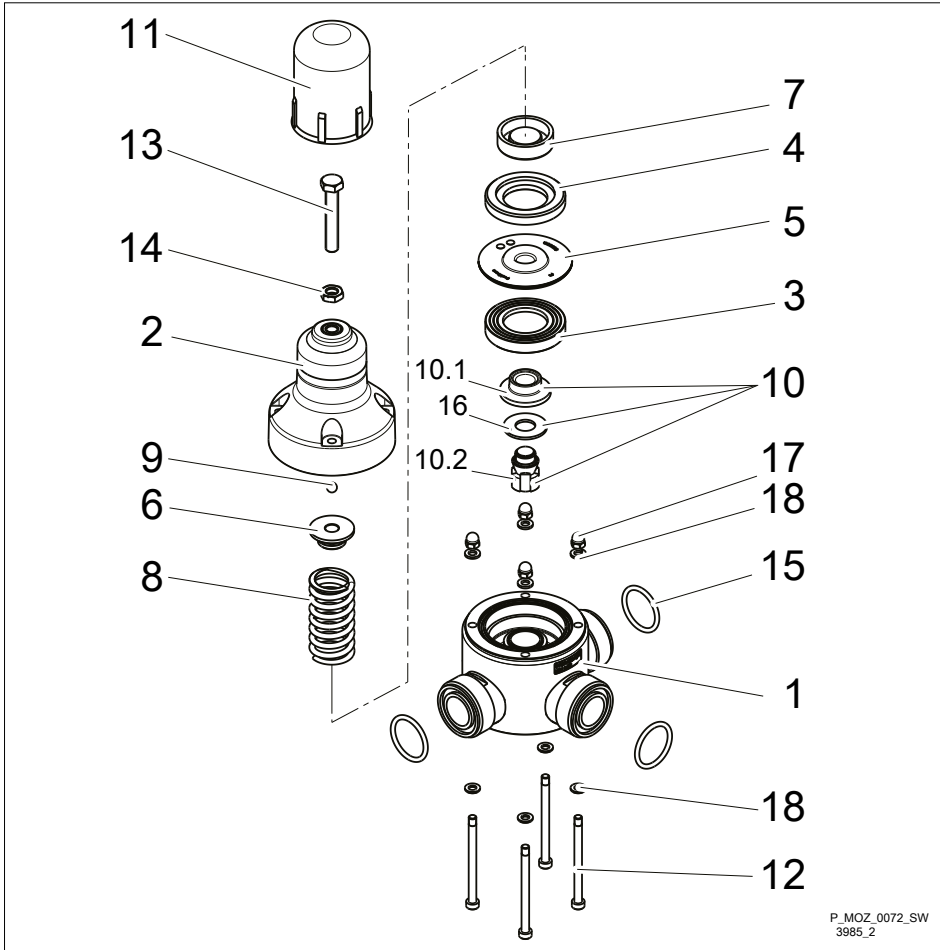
Explosionszeichnung DHV-UR PP_, PC_ und PV
